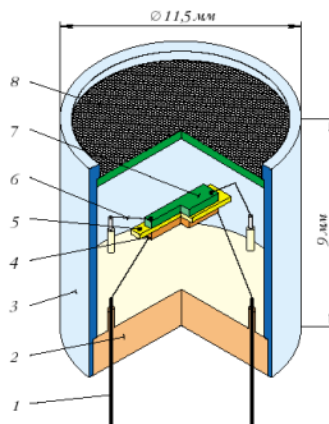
Структура резистивного газового сенсора: 1 – електронні виводи, 2 – панель зі скла, 3 – металевий корпус, 4 – нагрівальний елемент, 5 – підкладка, 6 – проволока, 7 – сенсорний елемент, 8 – противибухова металева сітка [3]
